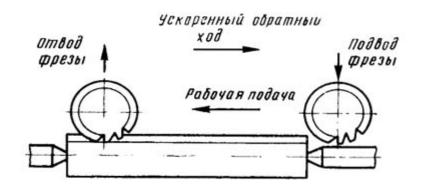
Автоматический цикл шлицефрезерного станка 5350А
